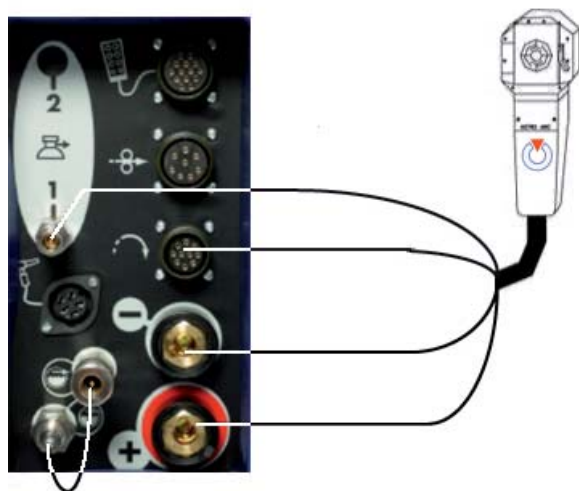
Anschluss einer luftgekühlten geschlossenen Schweißzange
